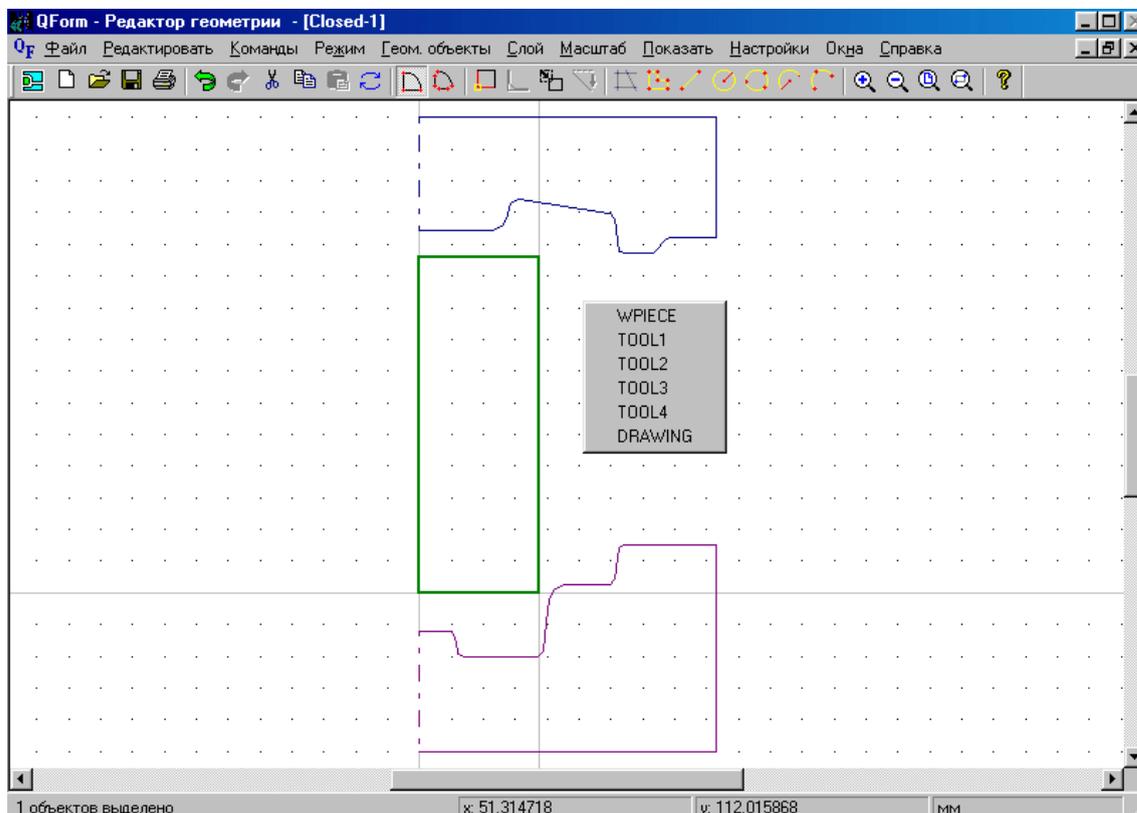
Контурные штамповых блоков и заготовки готовы для размещения на условных слоях
